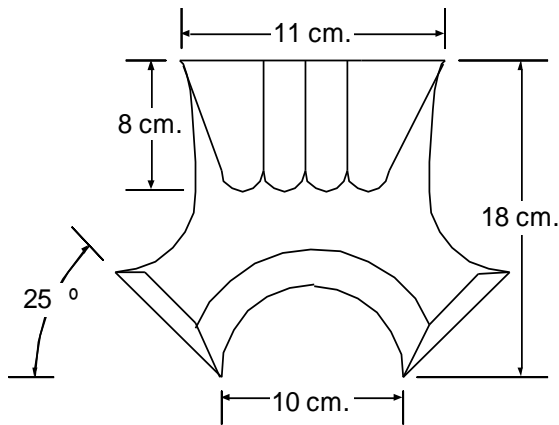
Corte transversal sección volante-guías arriba-abajo
